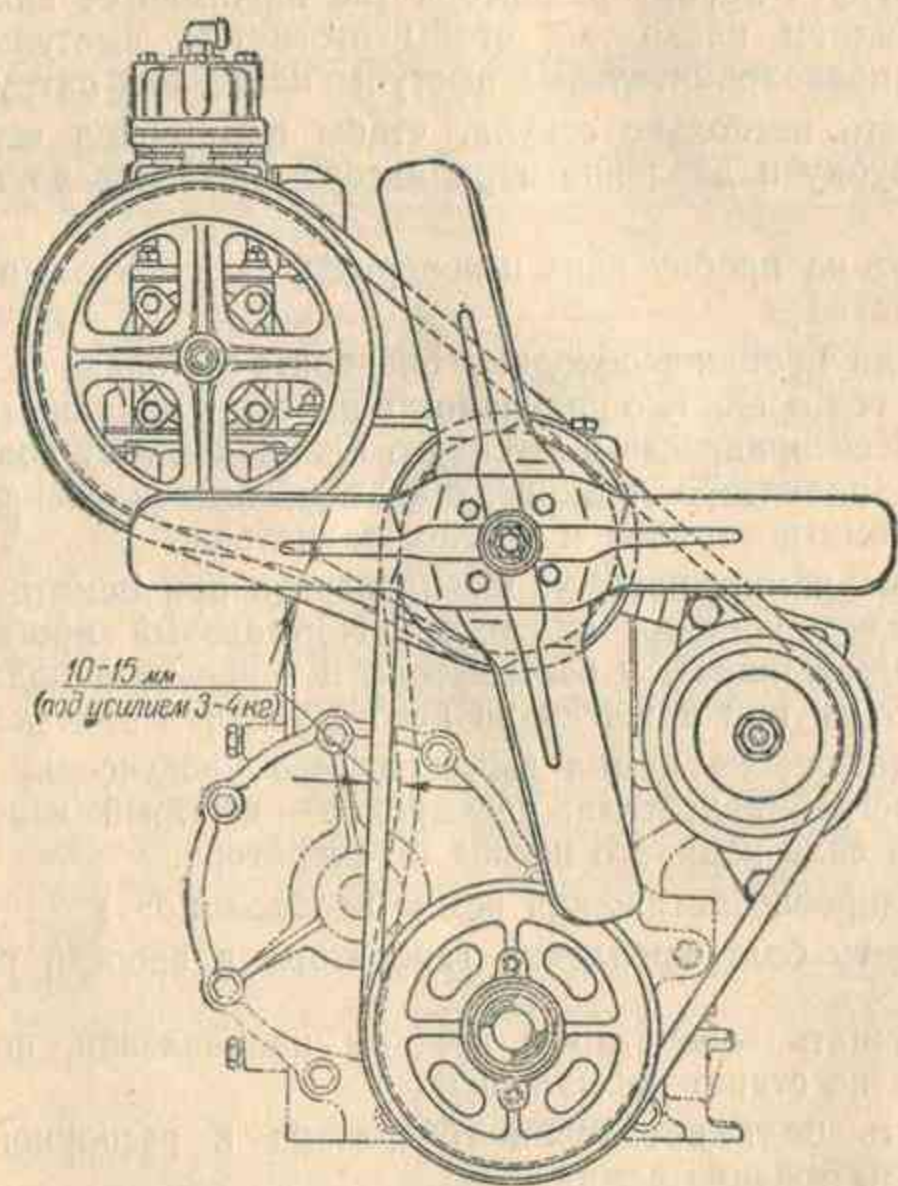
Проверка натяжения ремней привода вентилятора и компрессора
